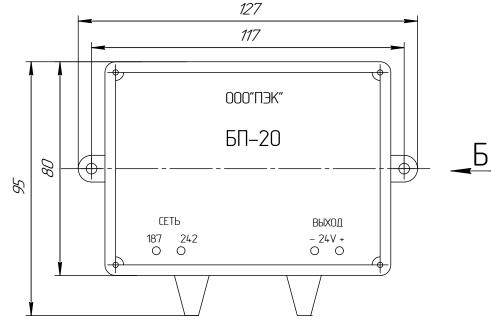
Габаритные размеры блока БП-20 (на DIN-рейке)
